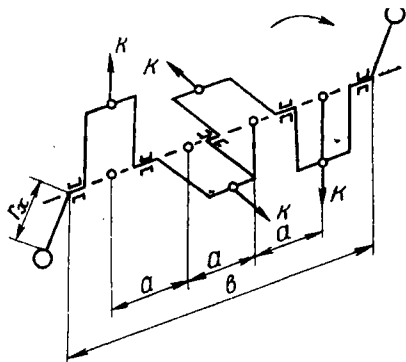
Схема коленчатого вала восьмицилиндрового двигателя с углом между цилиндрами 90° .
